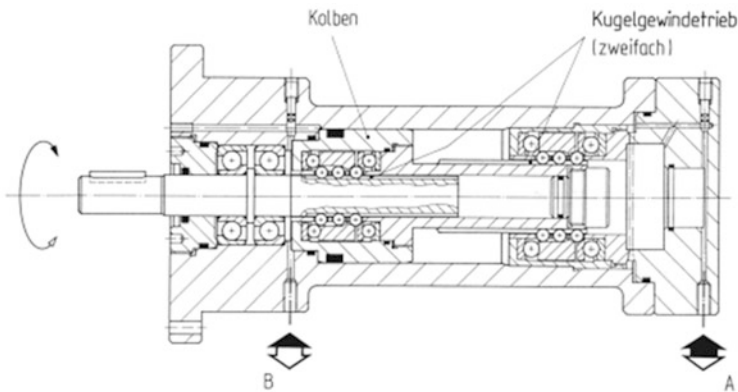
Kugelgewindeschwenkmotor (Bollmann)
